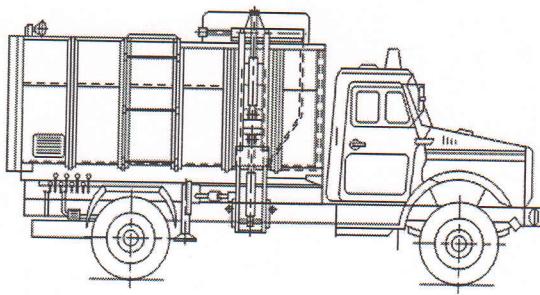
Кузовной мусоровоз с боковой загрузкой кузова манипулятором
